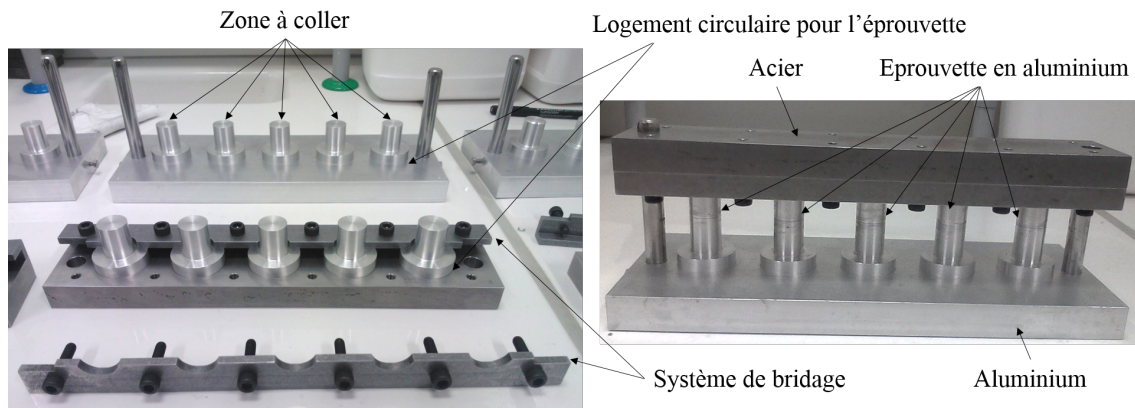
Montage permettant le collage des éprouvettes en aluminium
